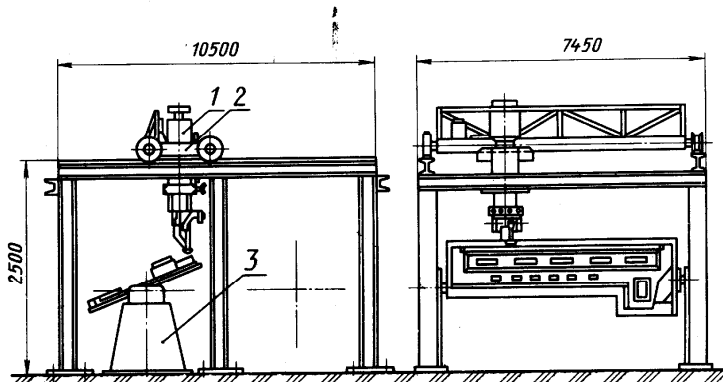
Портальная установка для сварки продольных швов боковых листов блока дизеля
